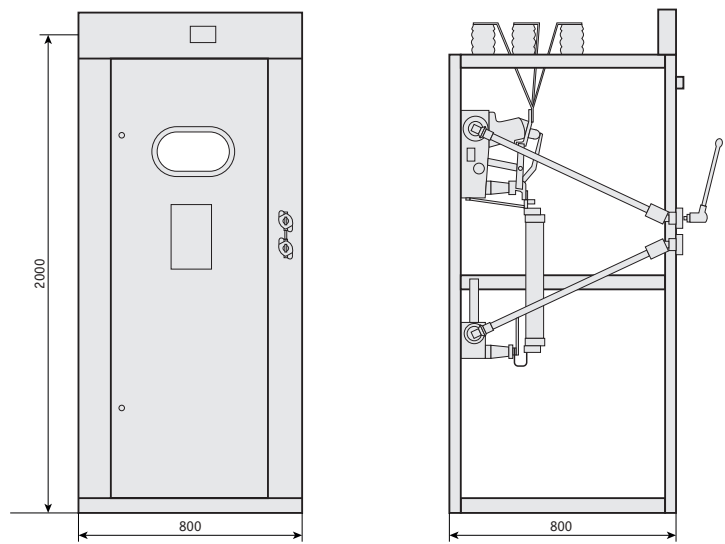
Габаритные и установочные размеры КСО-305 с ОМВ
